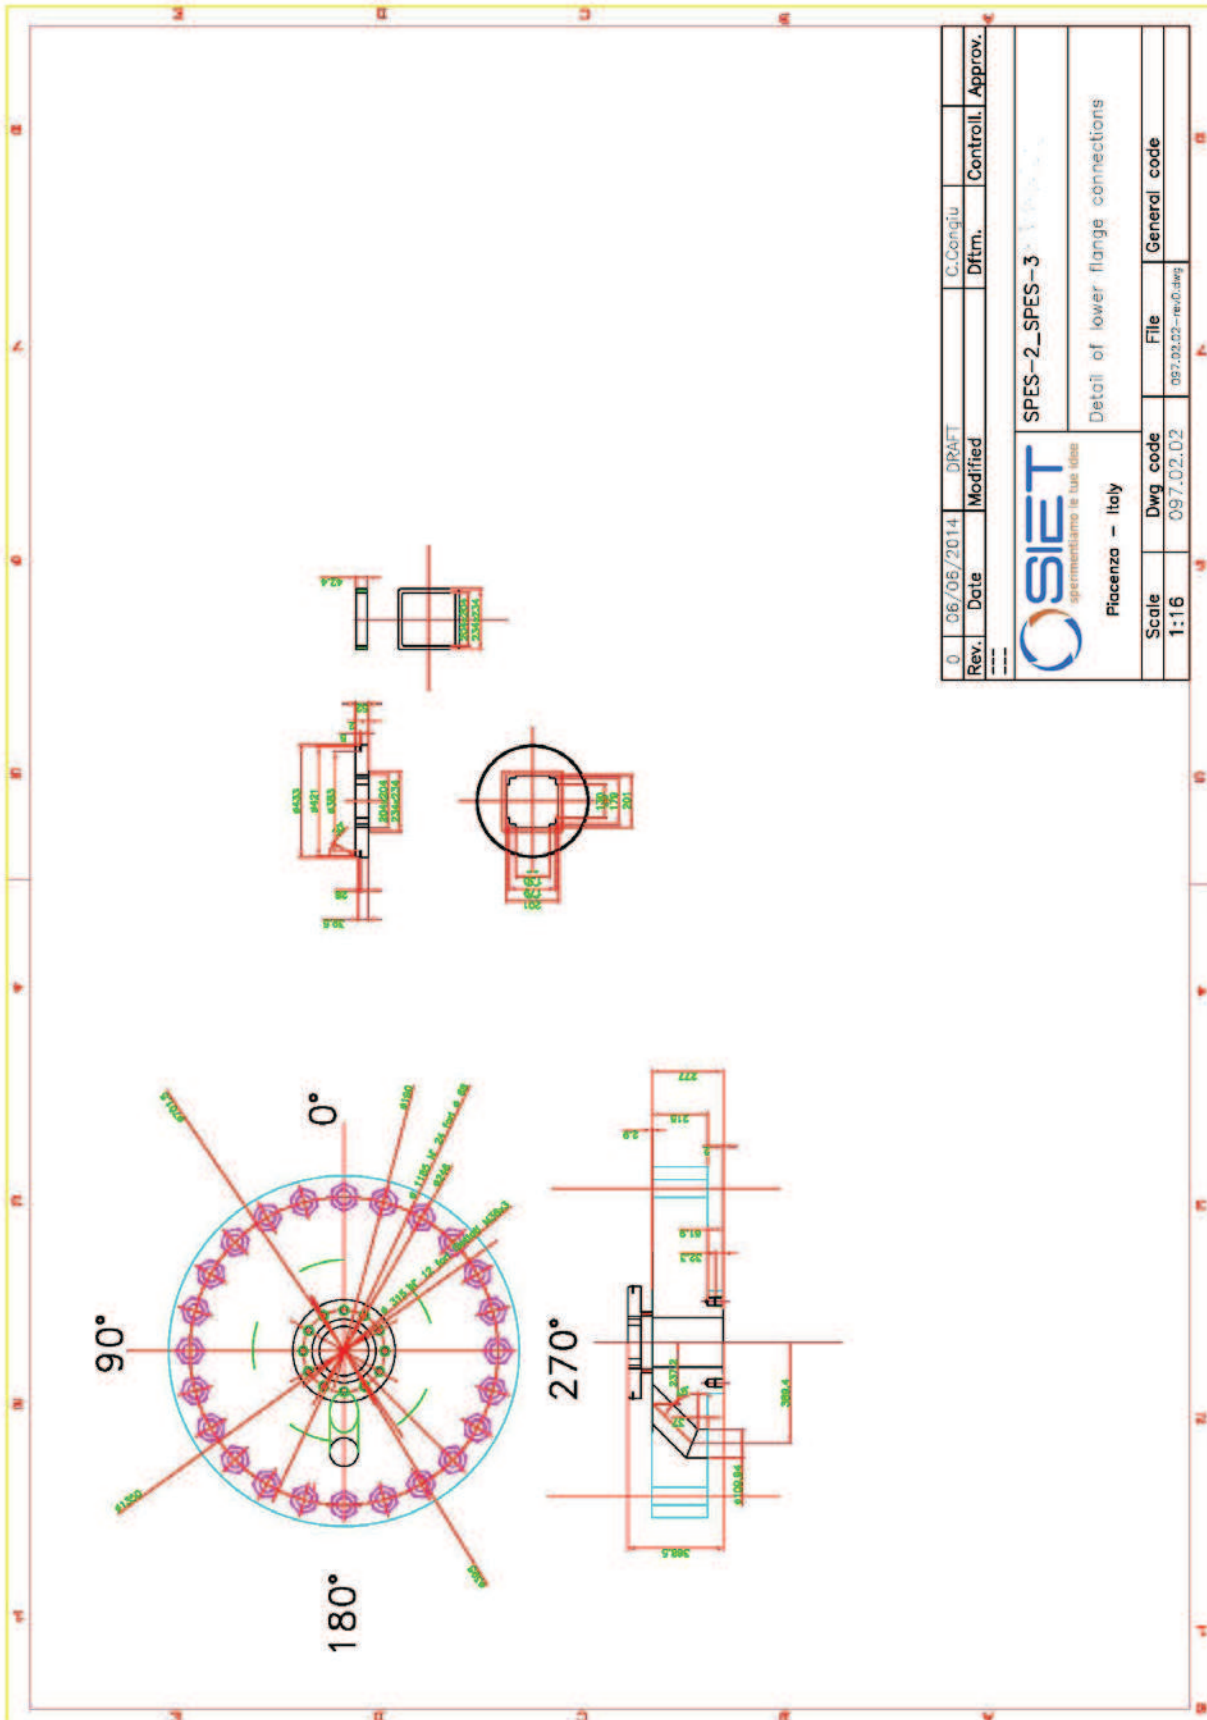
SPES-3, flangia inferiore di attacco riser - GV
